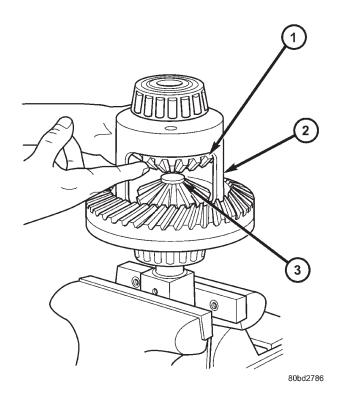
CONJUNTO DE EMBRAGUES Y ENGRANAJE LATERAL SUPERIOR
